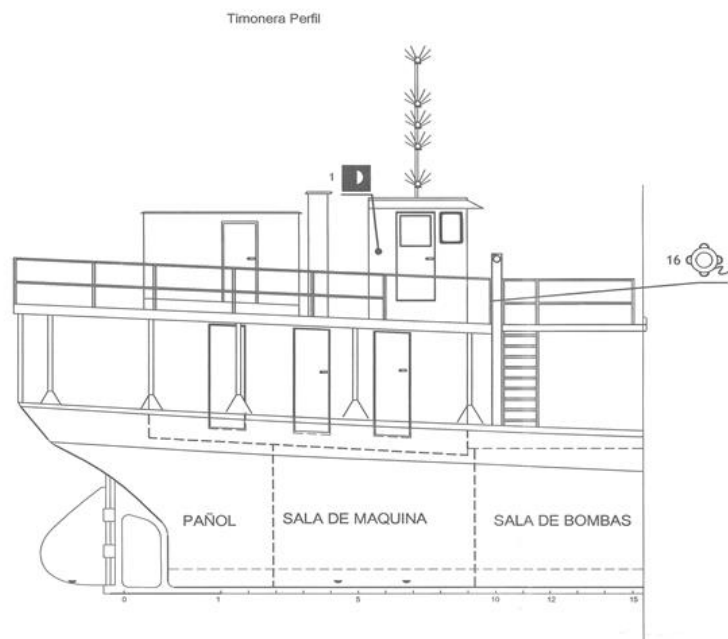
Plano de Armamento del B/M Fuerza del Destino. Vista perfil timonera (Año 2007)
